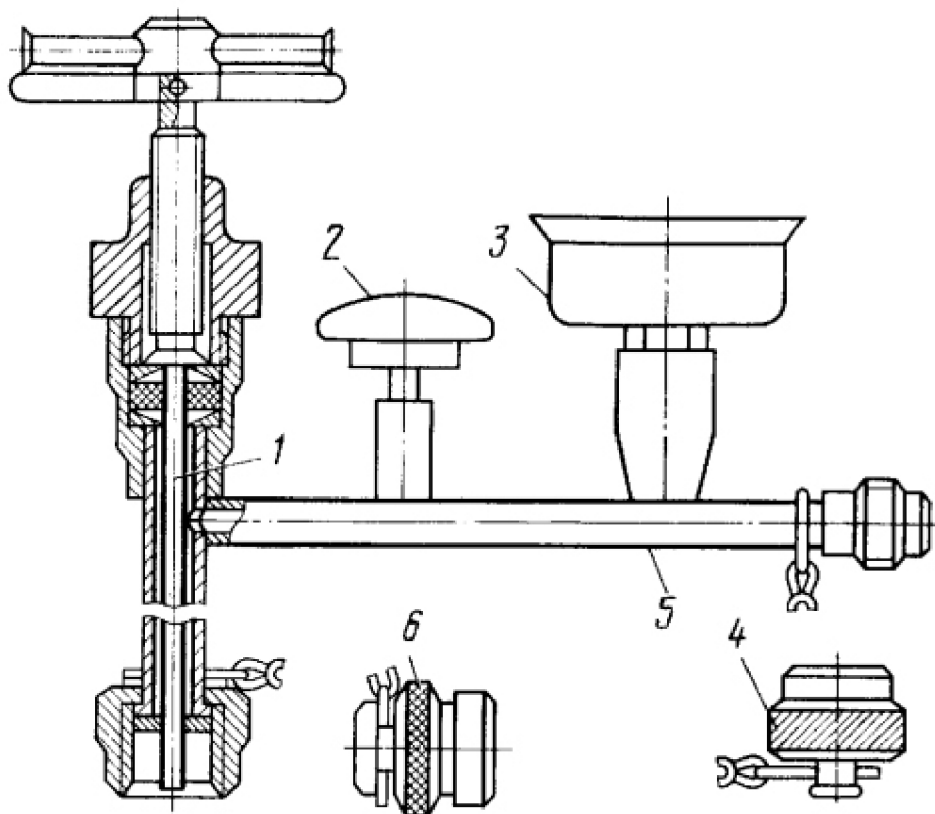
Приспособление для проверки давления и зарядки амортизатора шасси: 1- шток, 2-игла стравливания, 3-манометр, 4 - заглушка, 5 - корпус, 6 - пробка
